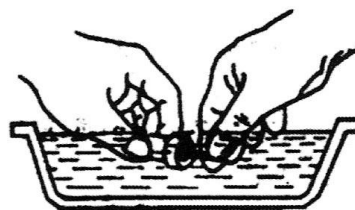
Промойте корпус форсунки и игольчатый клапан
